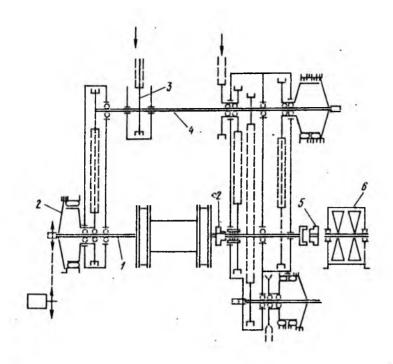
Кинематическая схема четырехскоростной лебедки У2-2-11 1 - подъемный вал; 2,5 - кулачковые муфты; 3 - звездочки; 4 - трансмиссионный вал: 6 - гидравлический тормоз
